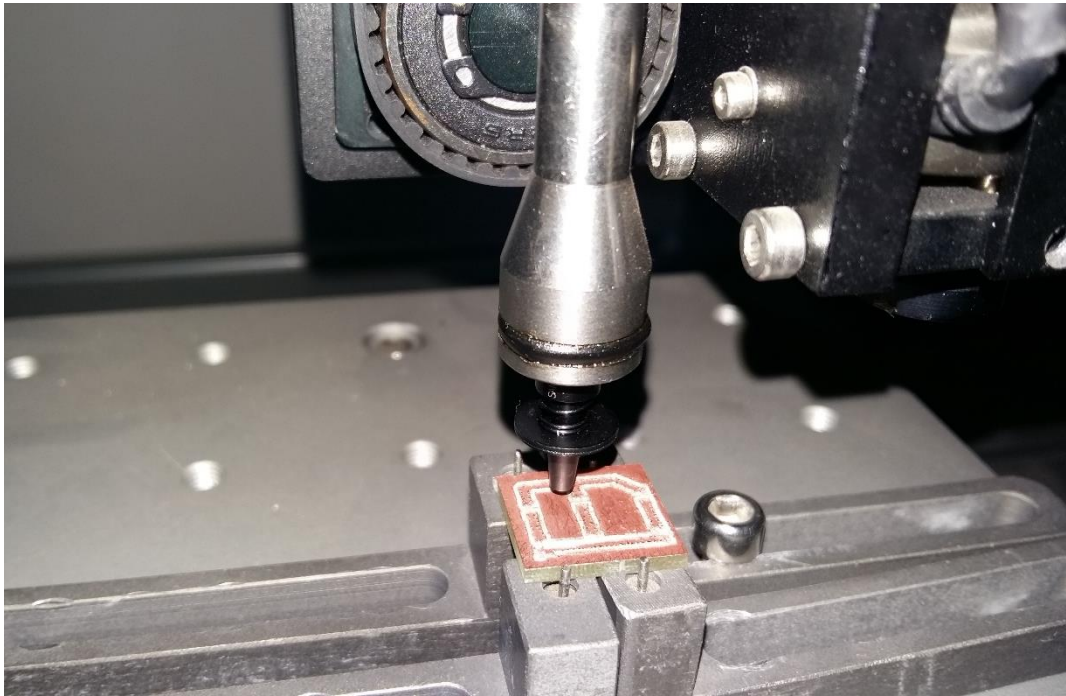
Pick and Place TP220 poniendo los componentes en la PCB.
